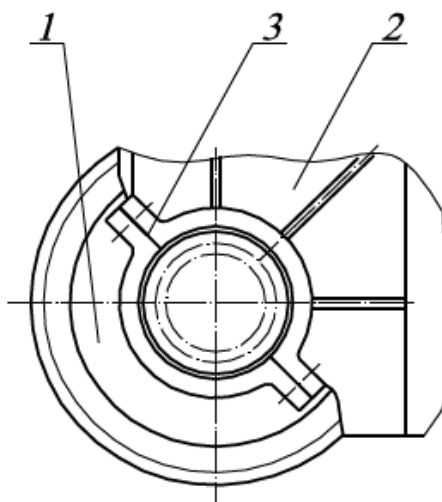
Конструкции ходовой части механизма передвижения крана:
